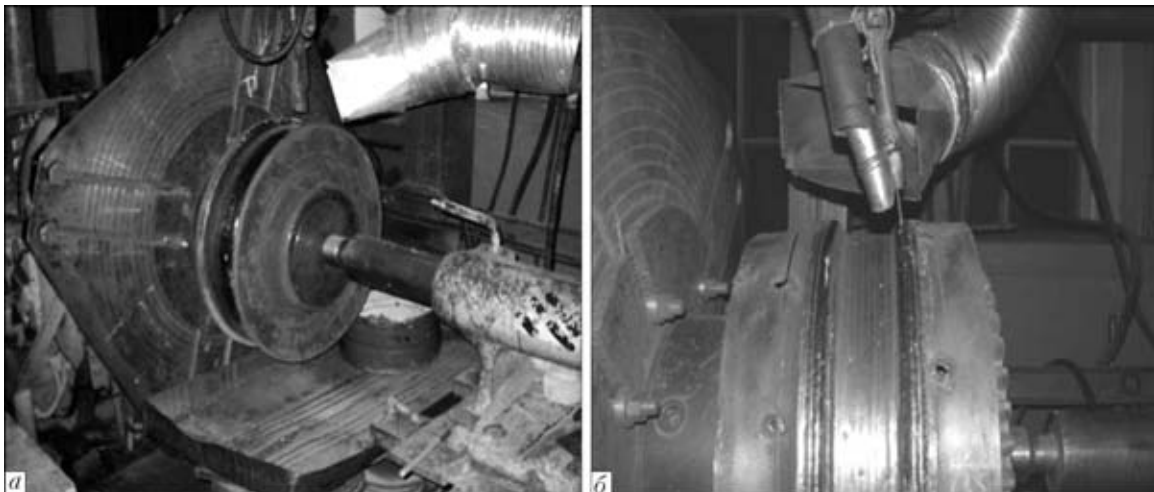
Автоматическая наплавка порошковой проволокой ПП-АН194 поверхности катания (а) и реборды (б) кранового колеса
